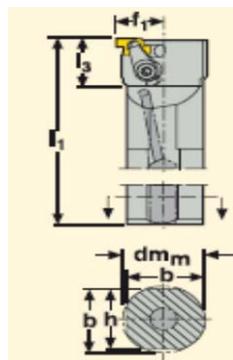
Державка токарная внутренняя CNR 0025R14A
